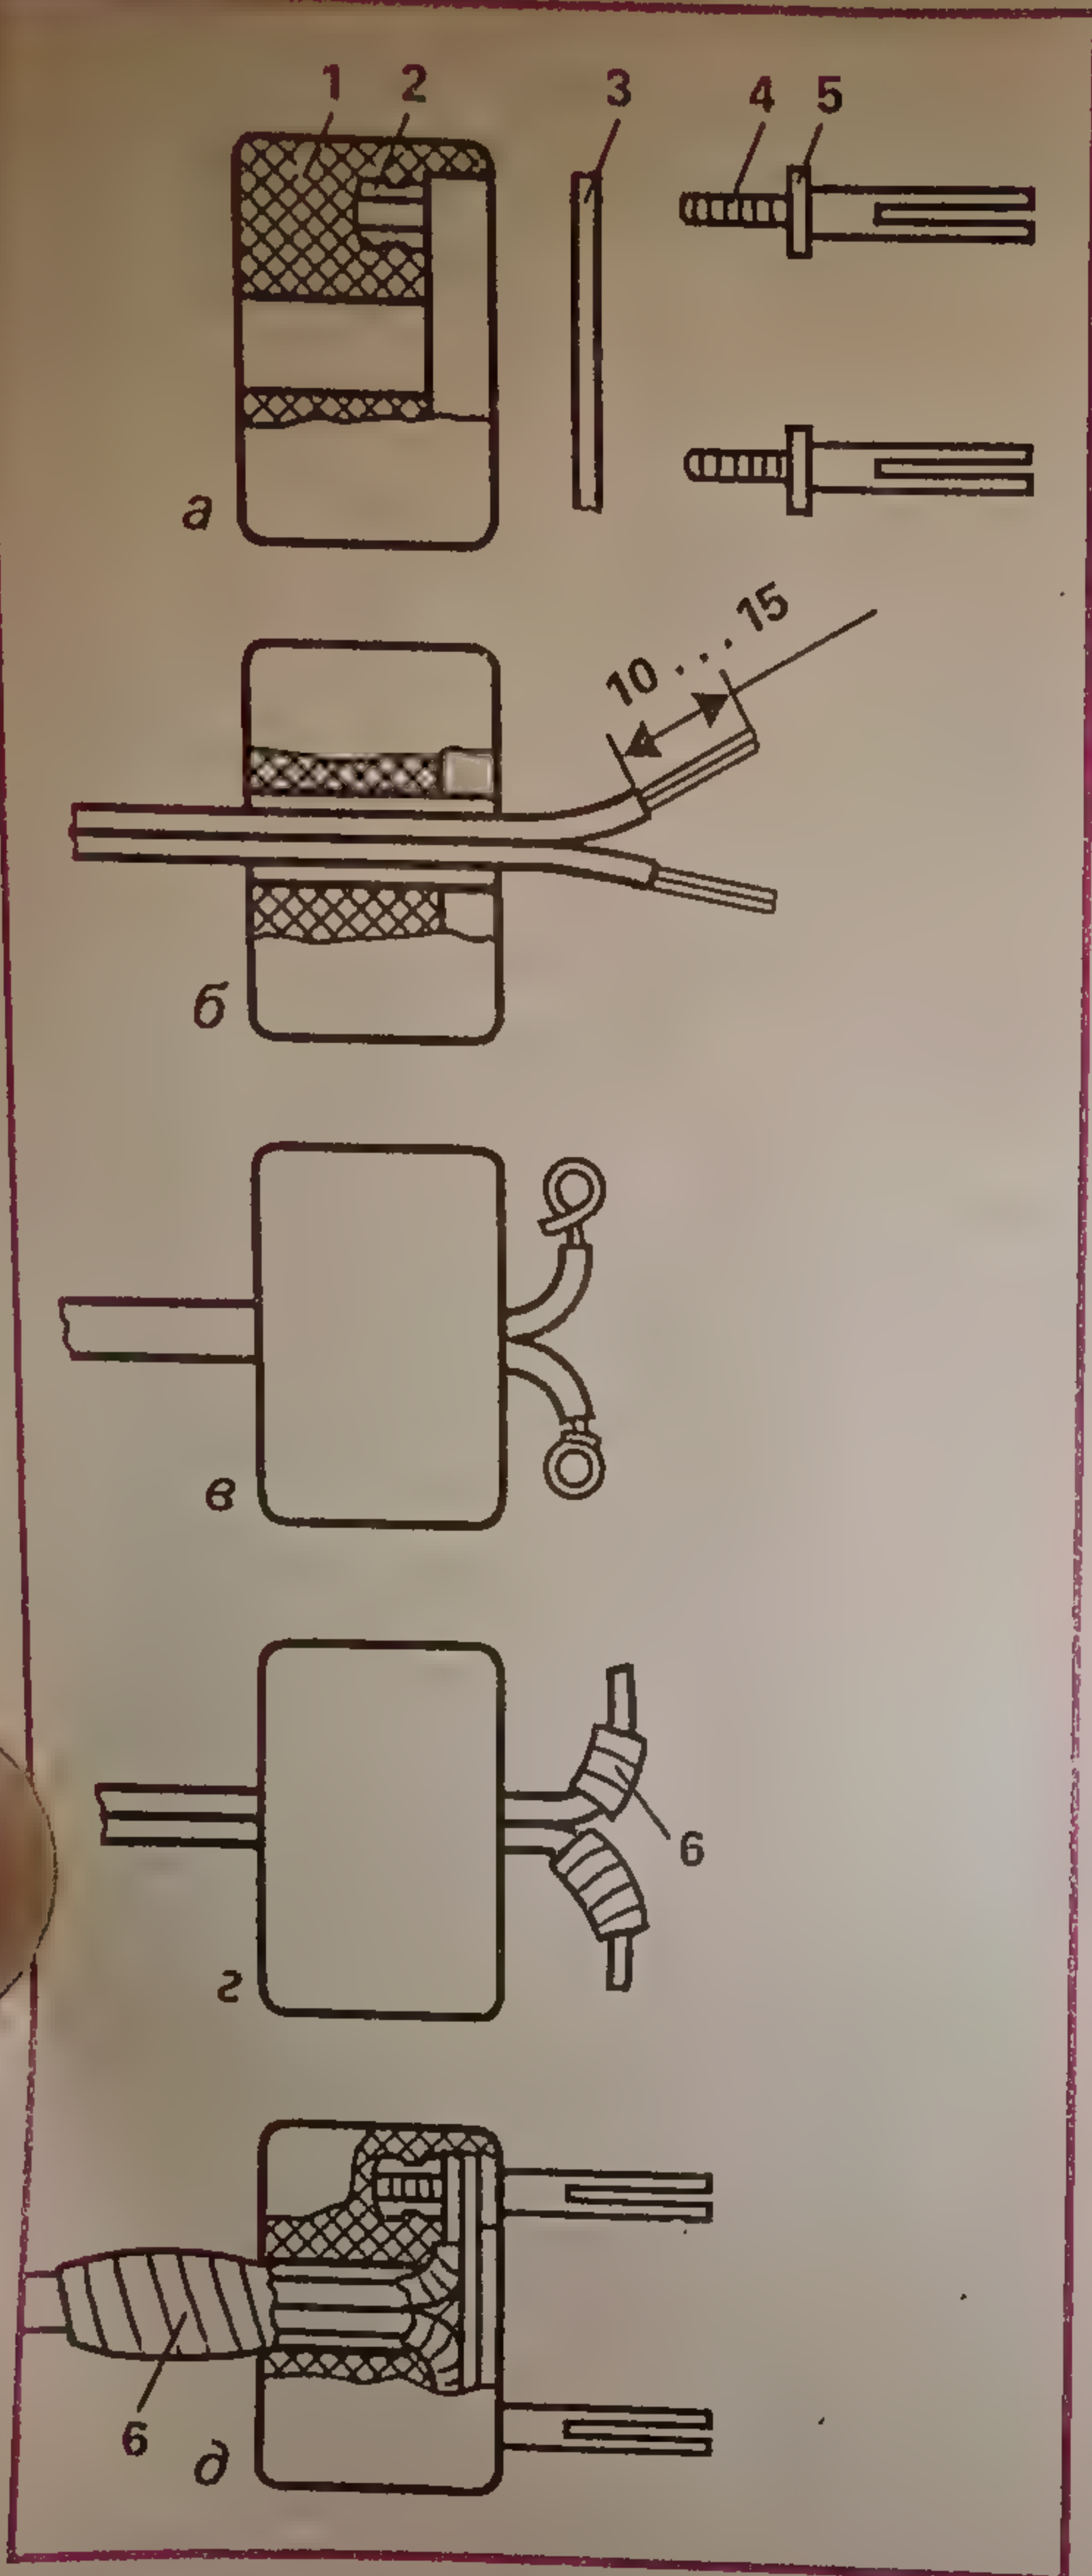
Монтаж и ремонт вилки с разрезными штифтами и цельным пластмассовым корпусом: 1 — корпус; 2 — спецгайка; 3 — планка; 4 — разрезной штифт; 5 — гайка шестигранная; 6 — изоляционная лента; а — разборка вилки; б — протягивание проводников сквозь отверстие корпуса и очистка от изоляции жил на длине 10...15 мм; в — загиб концов жил без изоляции в петли; г — место закручивания конца жилы, образующей петлю, изолируют; д — накладывание на петли планки и закручивание штифтов в спецгайки
